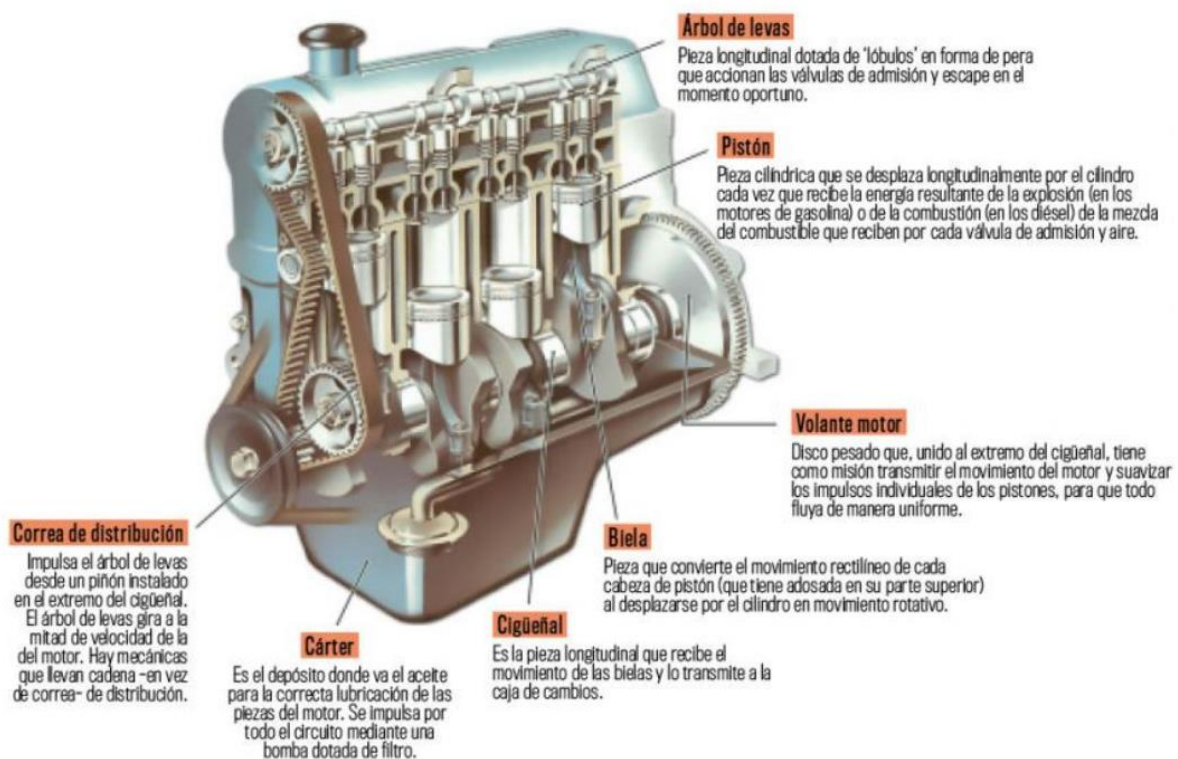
Parts d'un motor de combustió interna. Font: (11)
